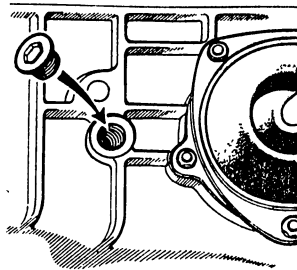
Пробка для заливки и контроля масла в коробке передач.
